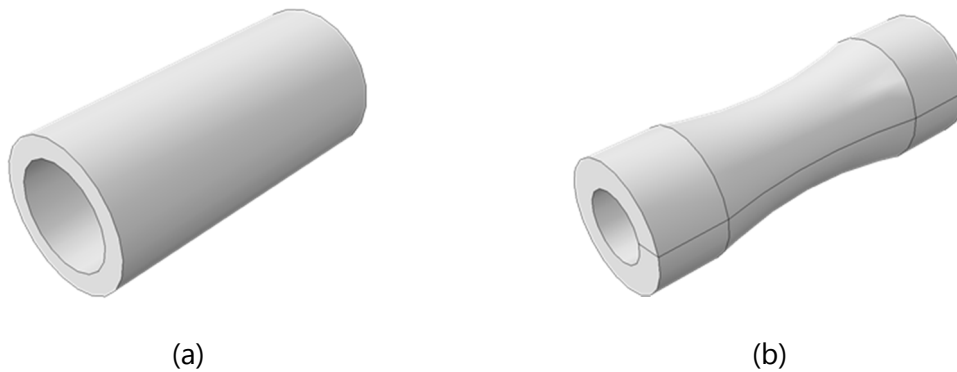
Wassergekühlte Hohlzylinder (3D-Modelle): (a) Hohlzylinder mit konstanter Wanddicke; (b) Hohlzylinder mit Hourglass-Kontour.
